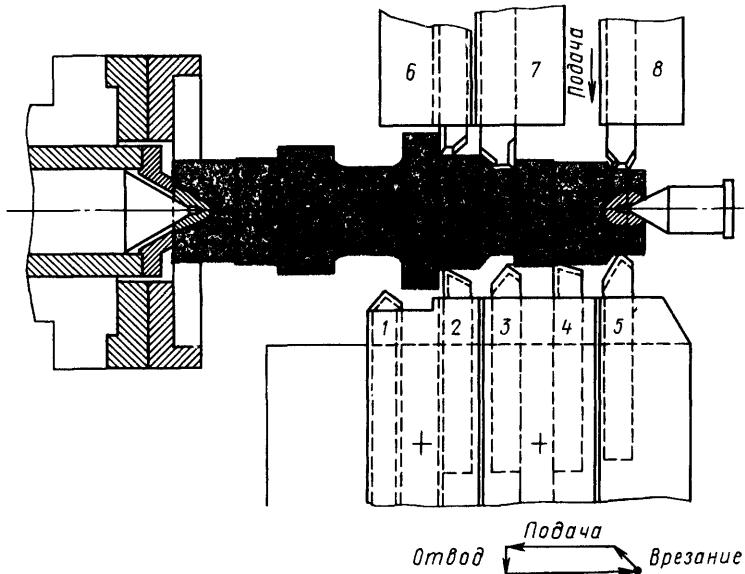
Схема наладки многорезцового станка на обработку ступенчатого вала
